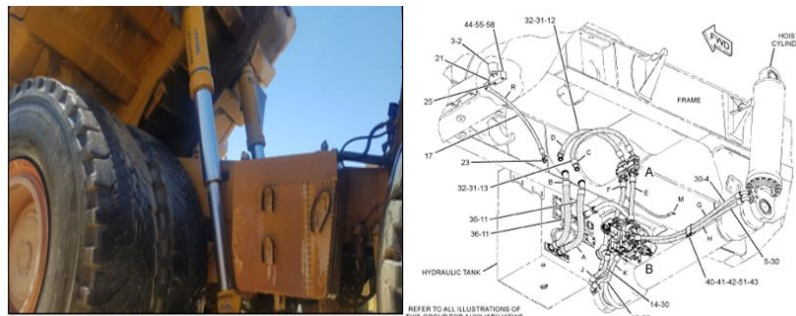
Inspección de fugas por vástago de cilindro de levante.
